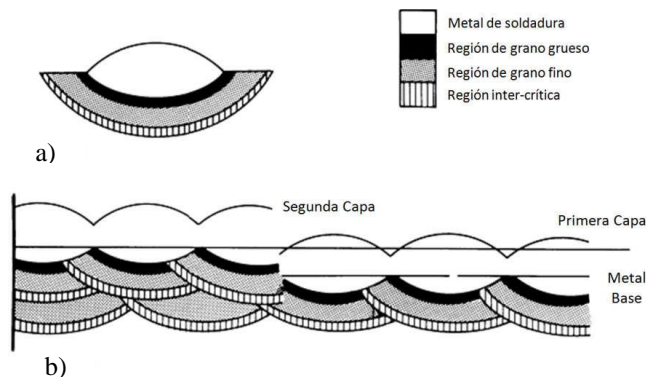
SOLDADURA DE REVENIDO. a) ZAT GENEADA EN EL PRIMER PASE DE SOLDADURA b) REFINAMIENTO DEL GRANO DE LA ZAT
